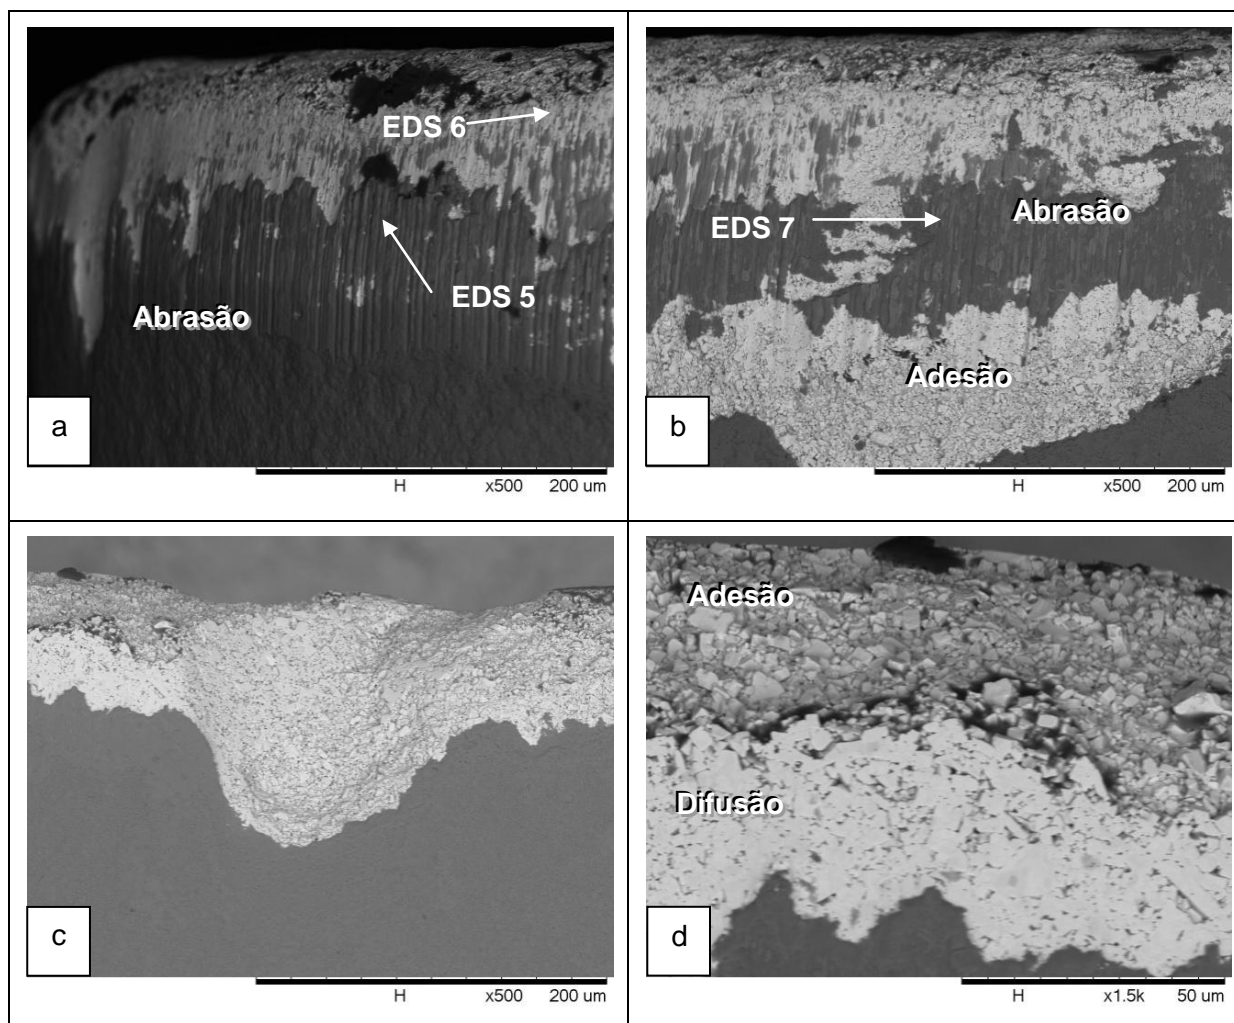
Detalhe dos mecanismos de desgaste presentes na superfície de folga da ferramenta utilizada para usinar o material B no ensaio de vida 1 ($v_c = 100,15$ m/min, $f = 0,35$ mm/volta e $a_p = 1,00$ mm). a) ponta da ferramenta; b) detalhe do flanco; c) entalhe; d) ampliação da região próxima ao entalhe
